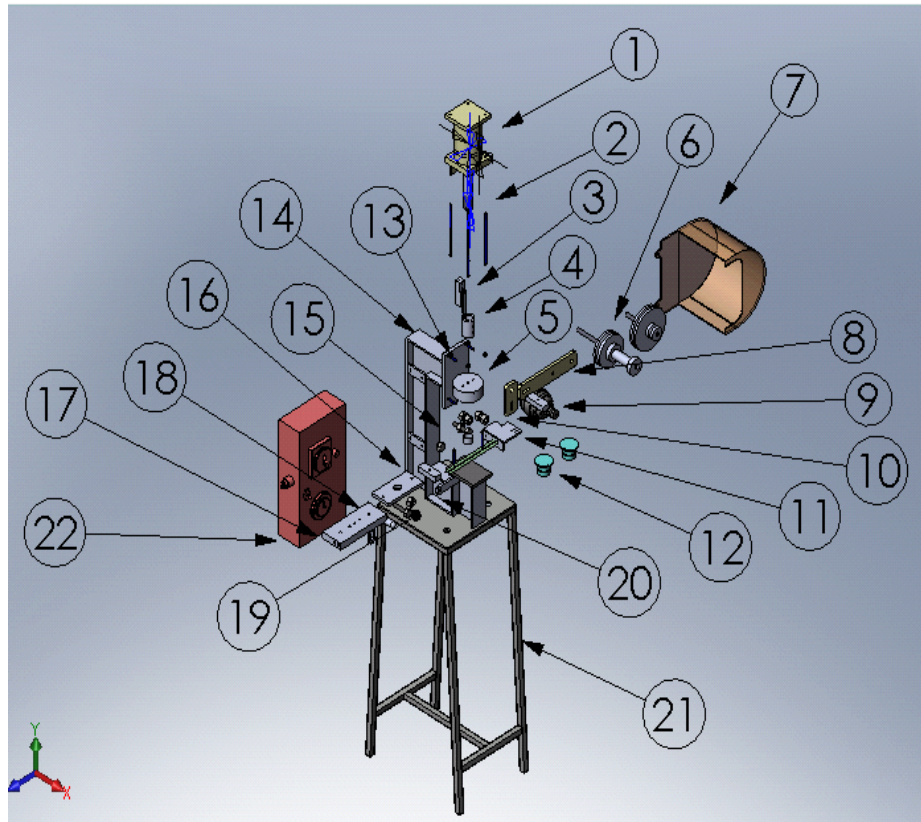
Despiece General de las Partes de la Máquina Selladora
